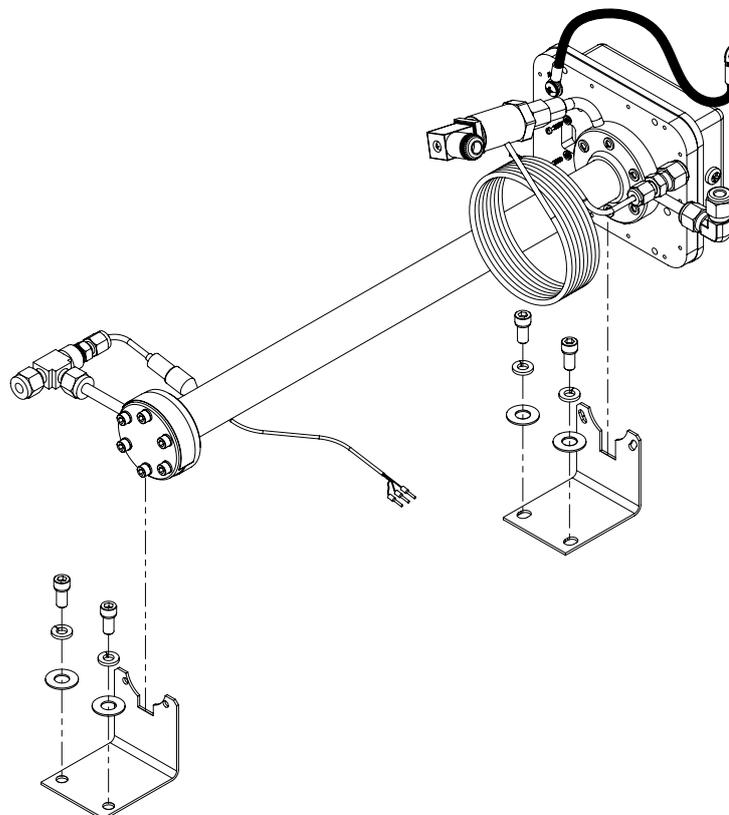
Zeichnung der Montagehalterung für die 0,8m-Messzelle
